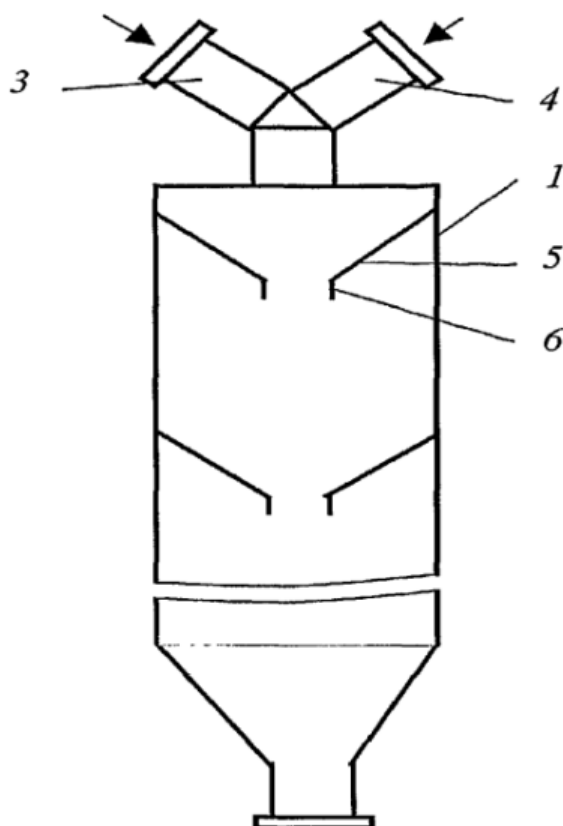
Конструктивна схема гравітаційного дозатора-змішувача: 1 – колона циліндрична; 3, 4 – завантажувальні патрубки; 5 - поверхні конічні; 6 - отвори
